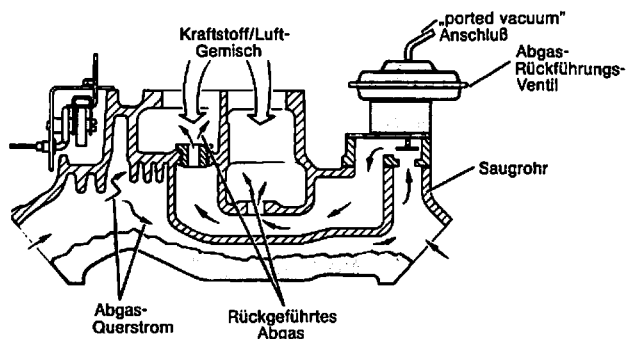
Das „floor jet“ Abgas-Rückführungssystem von Chrysler aus dem Modelljahr 1972, [621].
